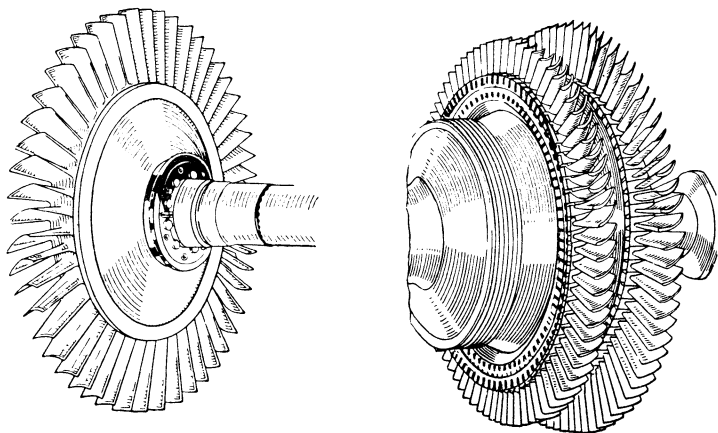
Так выглядит колесо газовой турбины, приводящей во вращение компрессор турбореактивного двигателя
